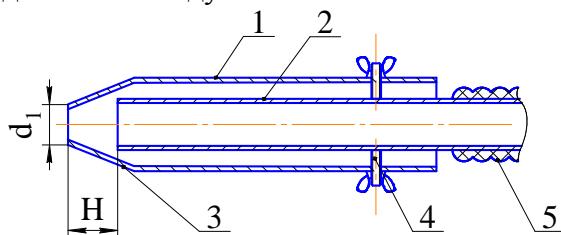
Конструктивная схема экспериментального эжектора: 1 – внешняя труба; 2 – внутренний патрубок; 3 – диффузор; 4 – регулировочные болты; 5 – транспортный трубопровод
